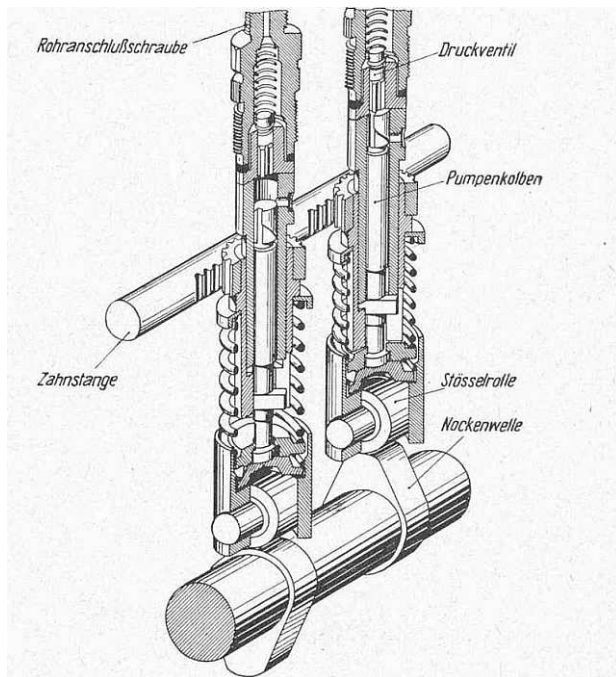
Schnitt durch das Pumpenelement der Scintilla – Einspritzpumpe (Schweiz)
